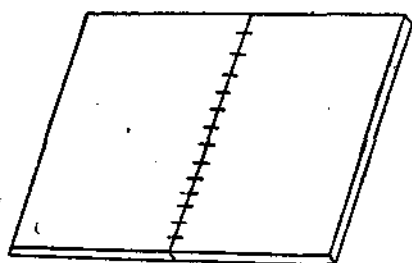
Подготовка к сварке алюминиевых листов просечкой кромок (двойной).
